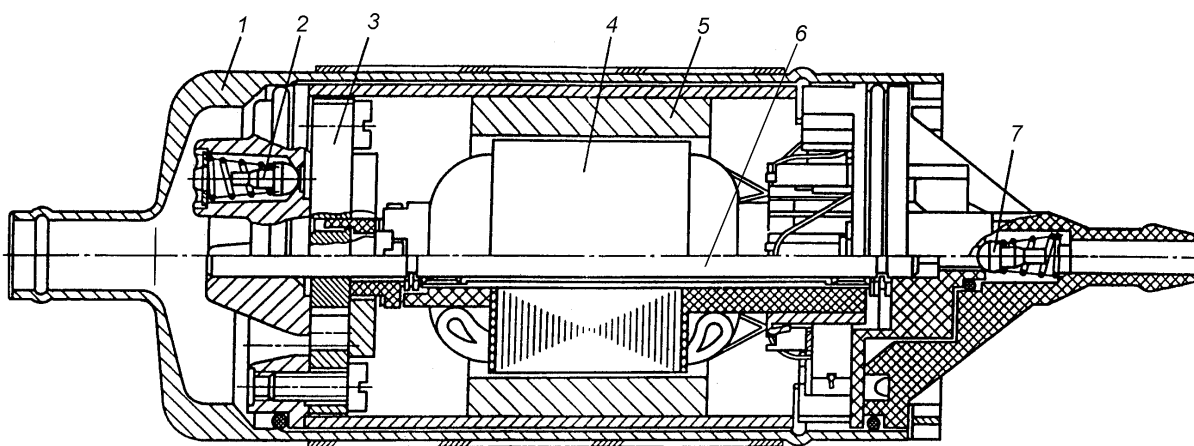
Конструкція підвісного бензонасоса: 1 – корпус насоса; 2 – запобіжний клапан; 3 – насосний вузол; 4 – якір електродвигуна; 5 – постійний магніт, 6 – вісь електродвигуна; 7 – зворотний клапан
